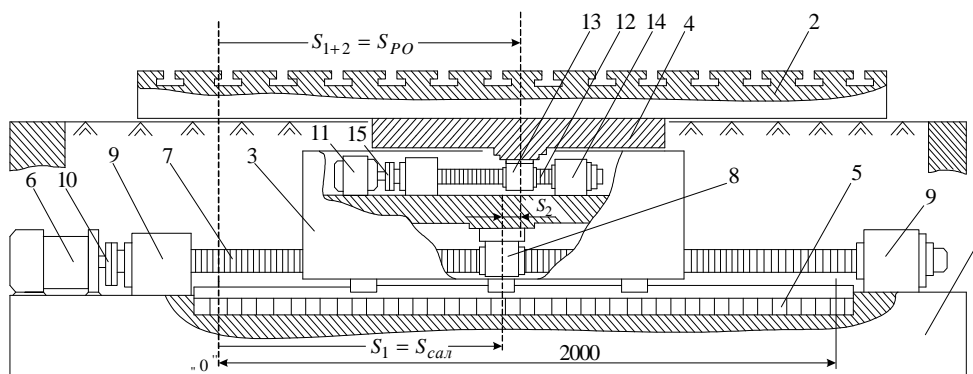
Вариант упрощенной схемы конструкции двухдвигательного безредукторного МП с двумя ВП для продольной (ось X) подачи РО (рабочего стола с изделием) металлорежущего станка
